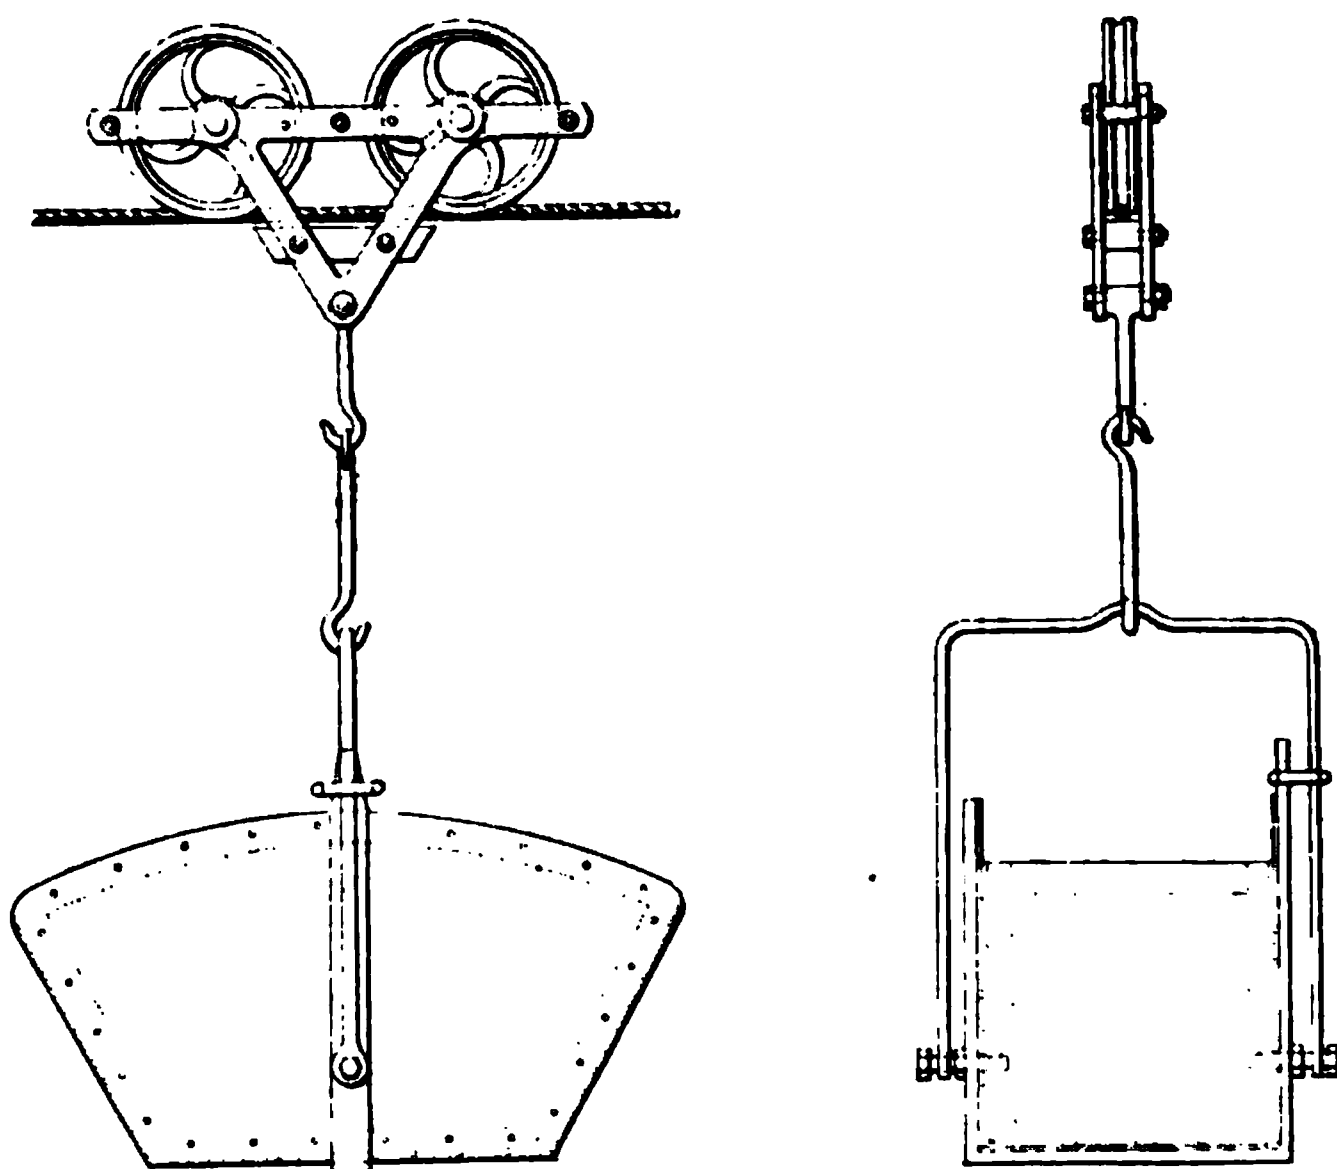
et 389. Plan aérien, système Balan (élevations latérale et antérieure).
